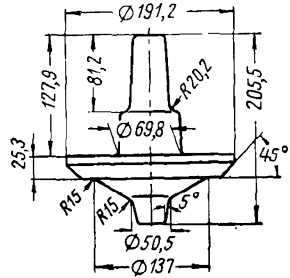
Молотовый штамп для поковки типа стержня с несимметричным фланцем
